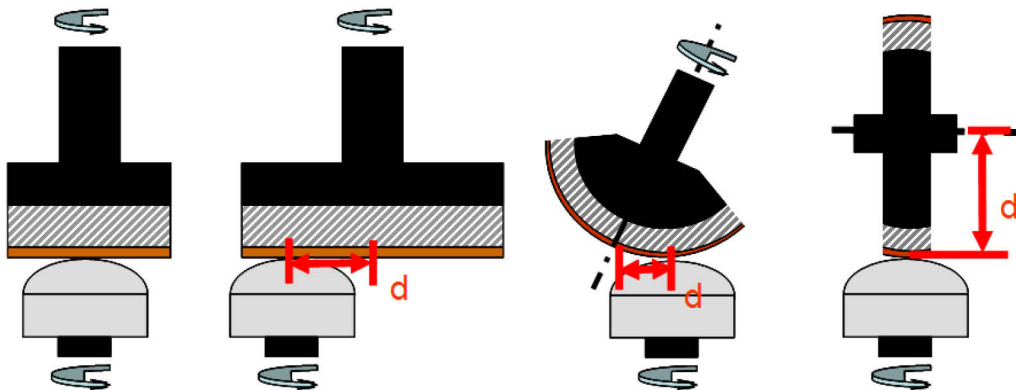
Padwerkzeuge, der Offset d ist als Abstand der Kontaktzone von der Drehachse des Werkzeugs in rot eingezeichnet, von links nach rechts: planes Werkzeug ohne Offset, planes Werkzeug mit Offset, sphärisches Werkzeug mit Offset, Radwerkzeug
